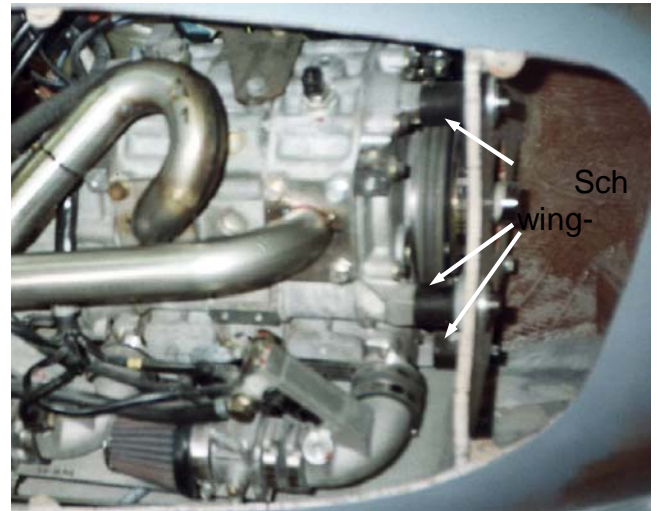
Befestigung des Motorblocks über Schwingelemente
